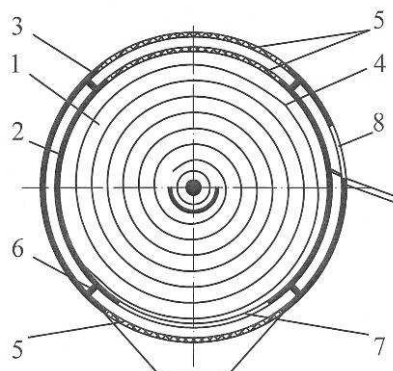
Сушарка з спіралеподібною поверхнею: 1 – сушильна камера; 2 – циліндрична обичайка; 3 – кожух; 4 – спіралеподібна поверхня; 5 – перфоровані вставки; 6 – поличка; 7 – вікно для вивантаження матеріалу; 8 – вивантажувальний отвір
